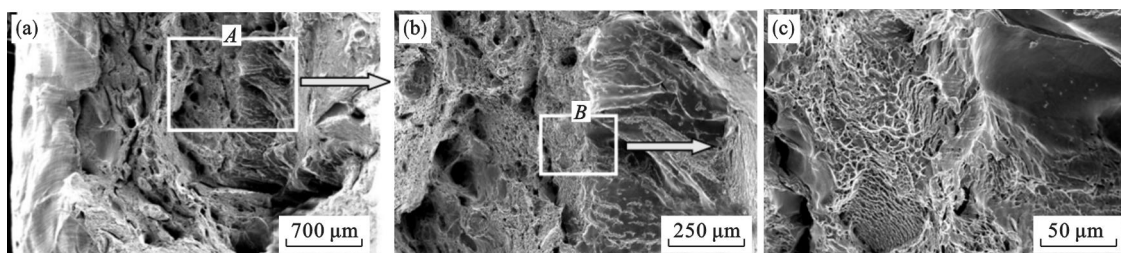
经 MIG 焊的 Fe-6.5% Si 合金热轧板在 500 °C 下的拉伸断口形貌
